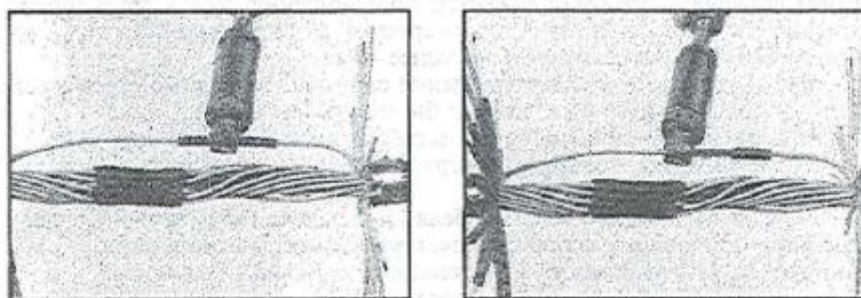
Усадка ТУТ на скрутке жил паяльником с насадкой
